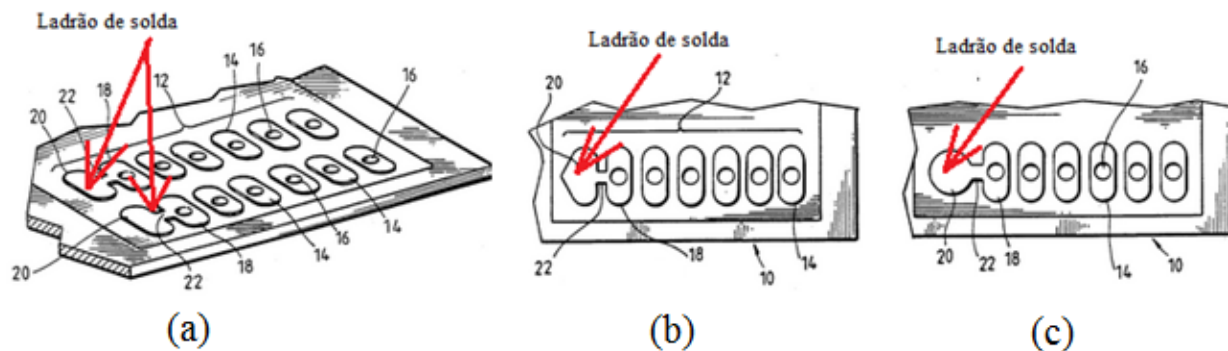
Exemplos de ladrão de solda: a) ladrão de solda separado da ilha de solda; e b) ladrão de solda como prolongamento da própria ilha de solda.
